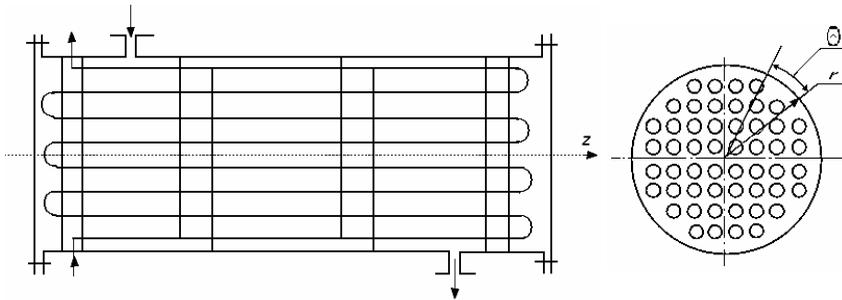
Схема типовой конструкции кожухотрубного аппарата
